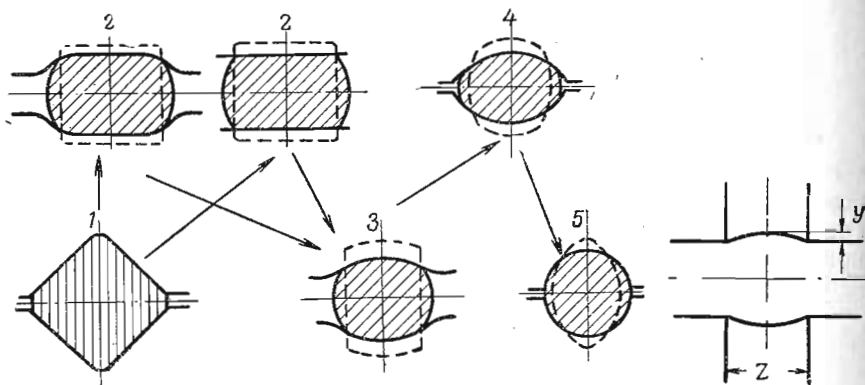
Схема прокатки круглой стали в системе калибровки квадрат — ступенька — ребро — овал — круг
